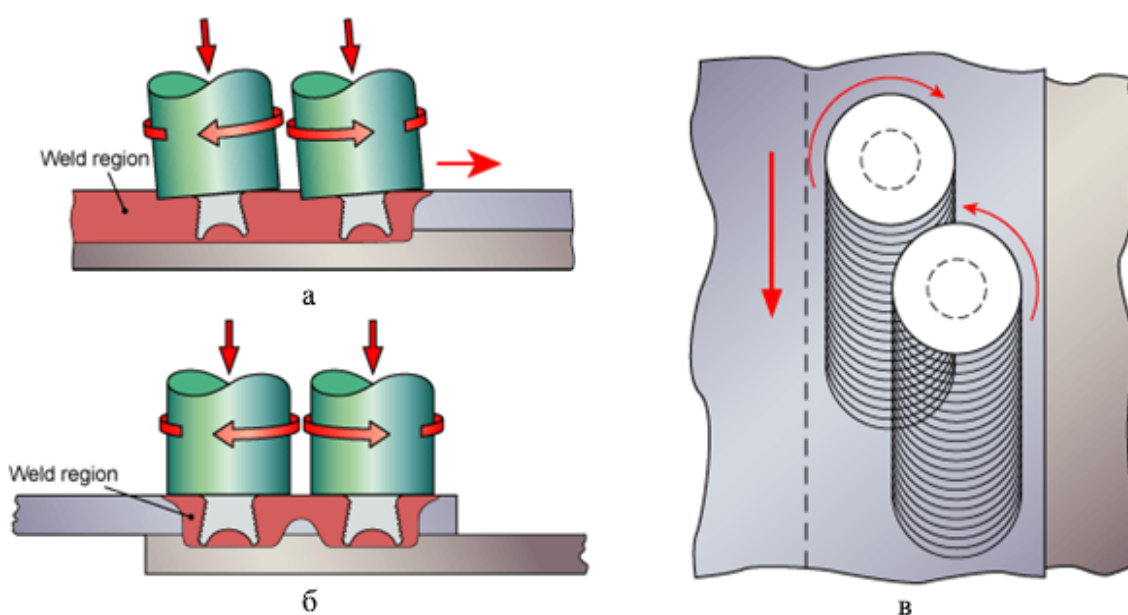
Схема СТП по технологии Twin-Stir™ [6] с последовательным (а), параллельным (б) и смещенным (в) движением сварочных инструментов [6]
